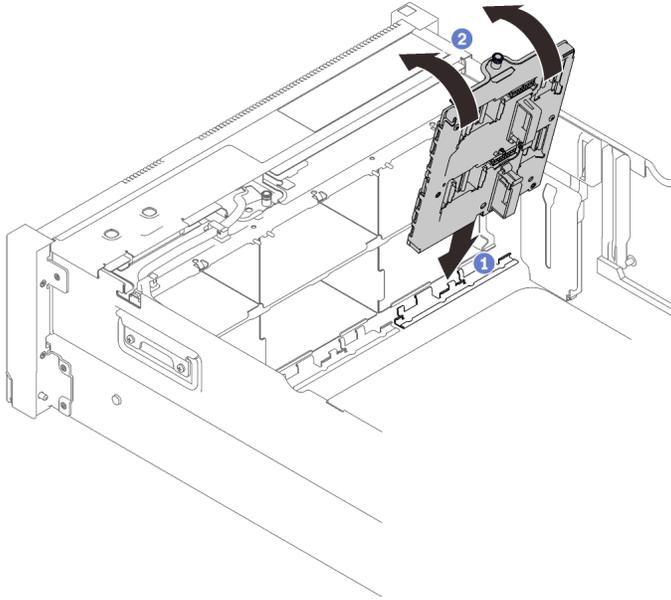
Installazione dell'assieme della piastra del backplane dell'unità
